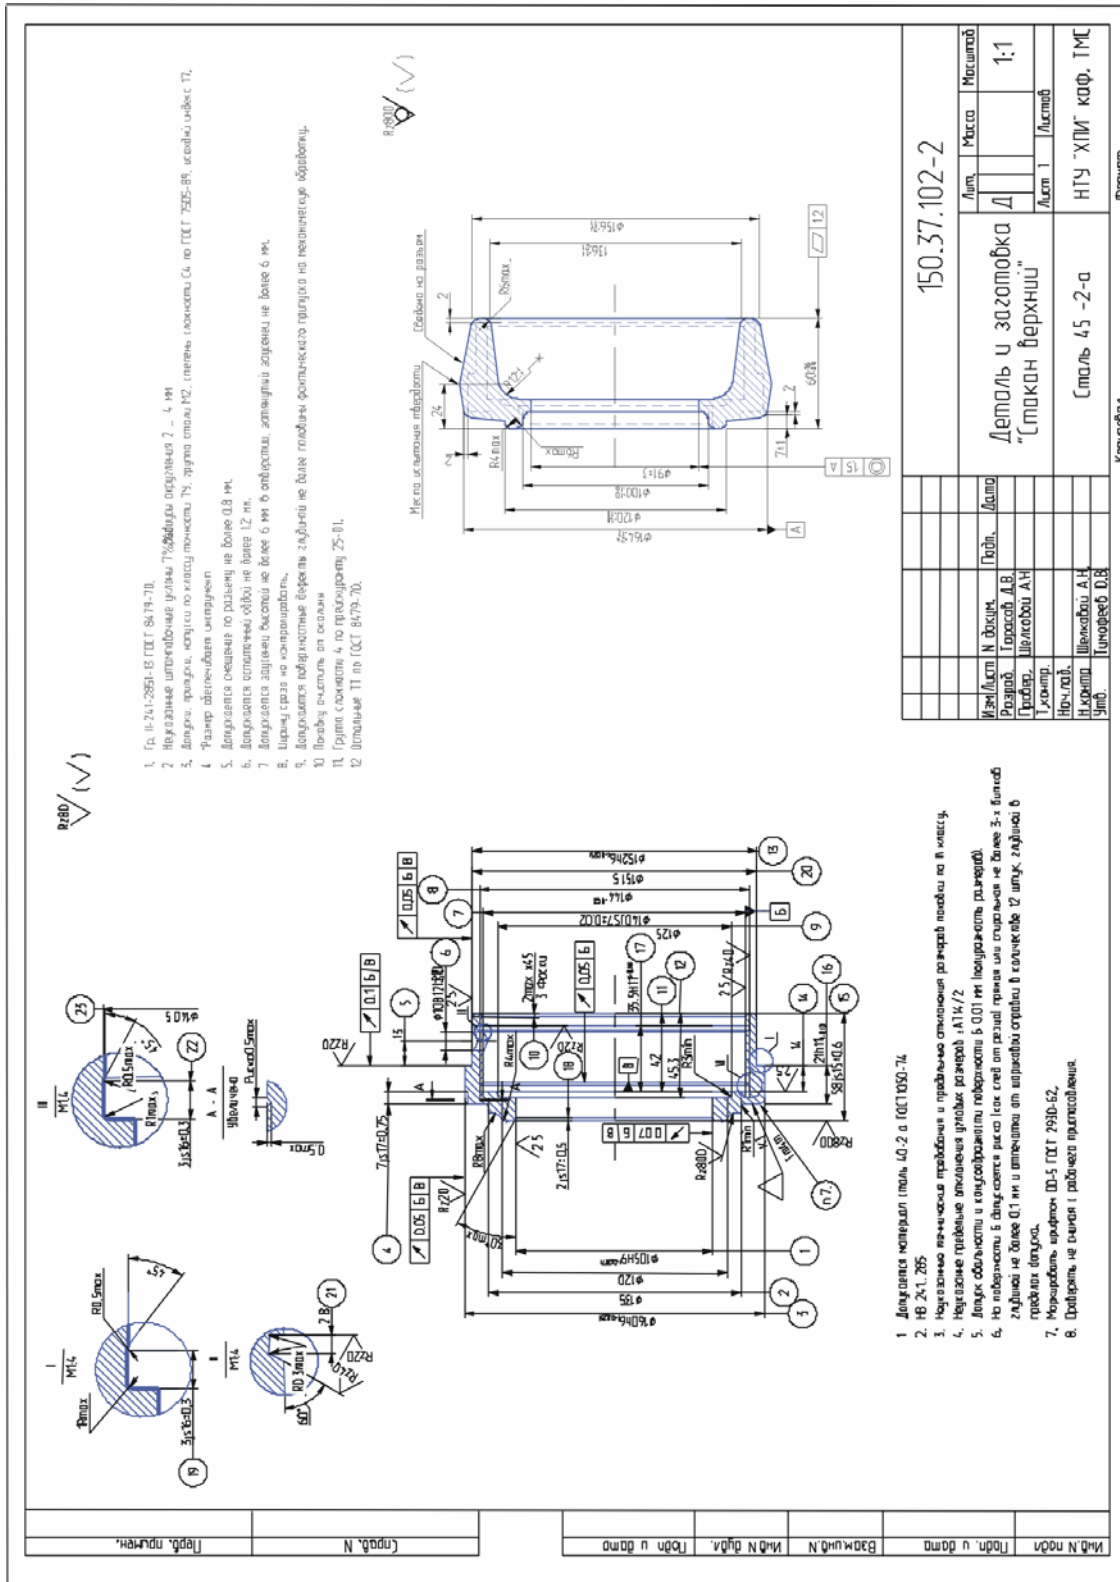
Чертежи деталі и заготовки изделия «Стакан верхний 150.37.102-2»
